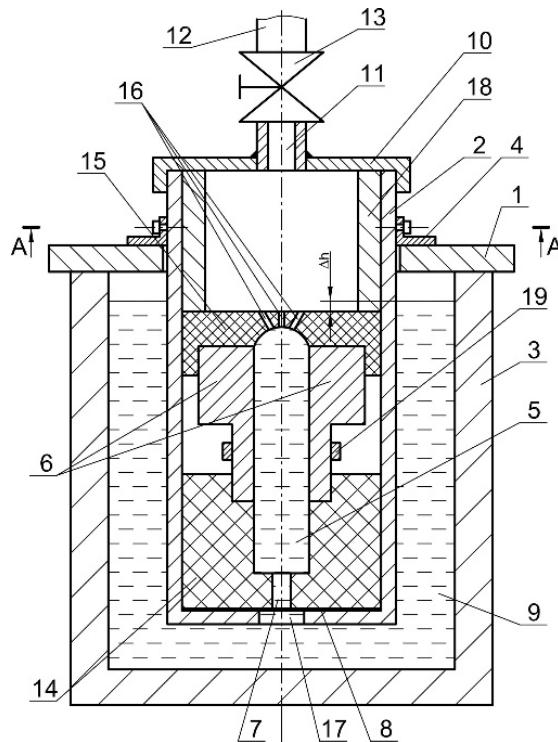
Схема переносного устройства для отбора пробы жидкого металла
